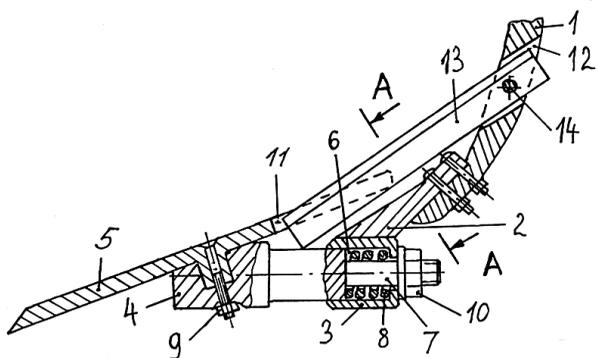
Рабочий орган культиватора (вид сбоку)
